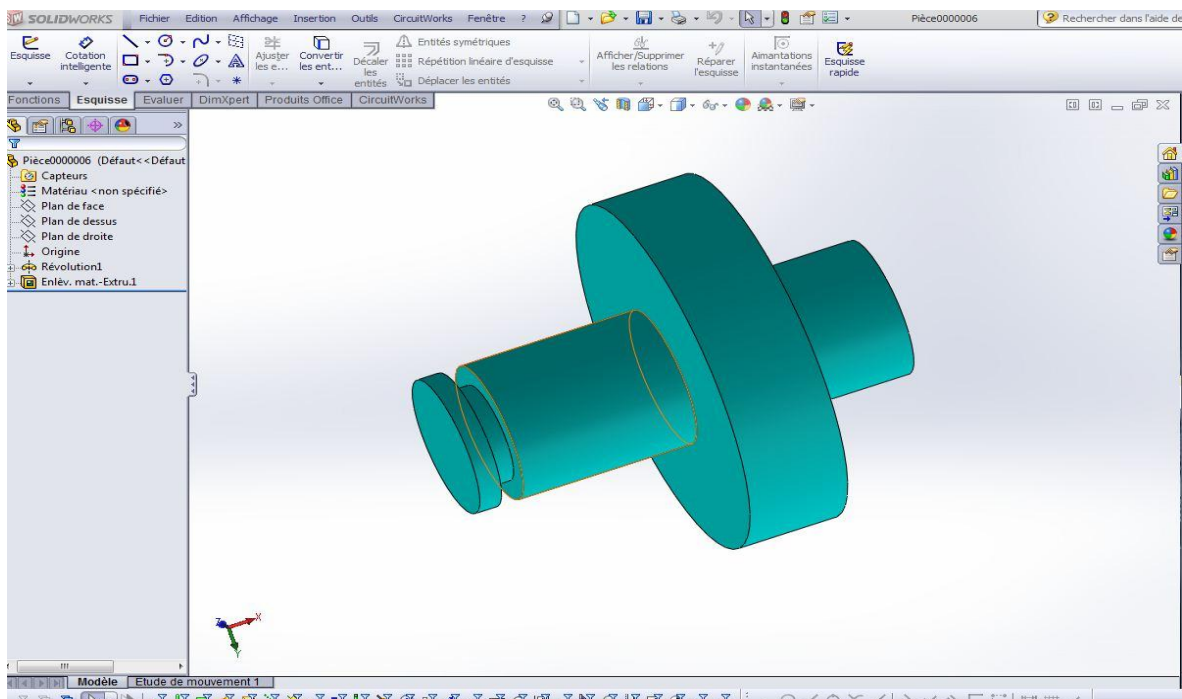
Vue Pièce pour fixe la Bielle avec Disque et arbre rotatif réalisée sous SOLIDWORKS
